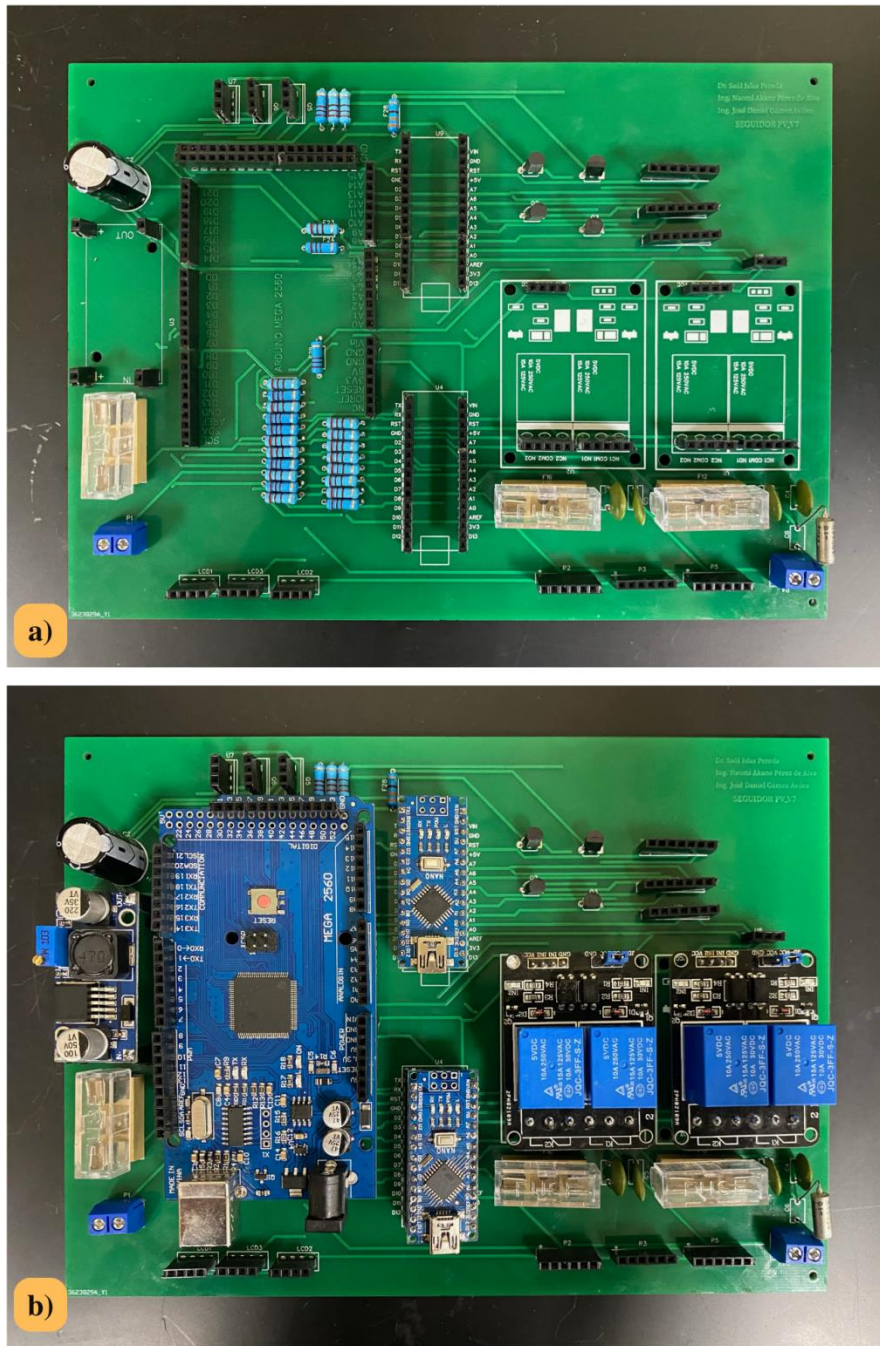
a) Placa de circuito impreso soldada. b) Placa de circuito impreso con los componentes insertados.
